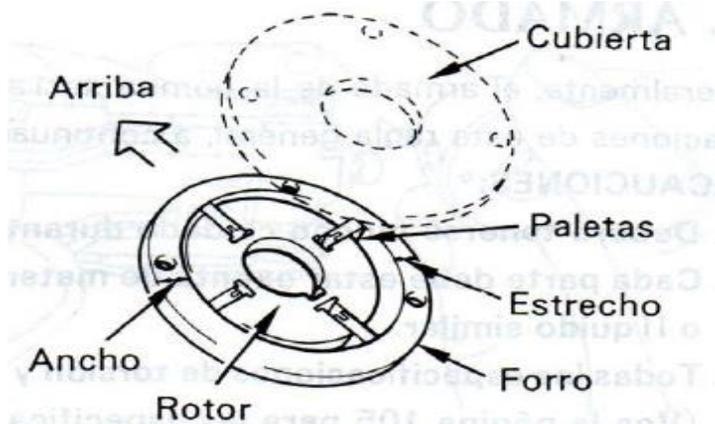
Montaje del conjunto de la bomba de alimentación.
